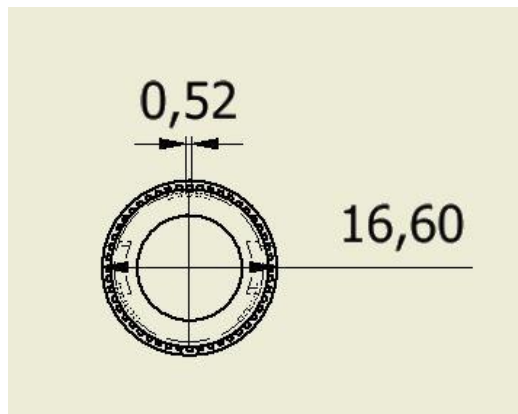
Tampak dalam *greaser shell* hasil *redesign
